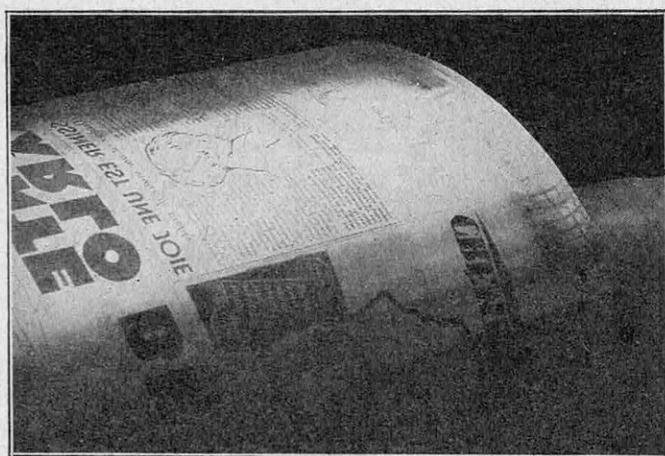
VUE D'UN CYLINDRE GRAVÉ
